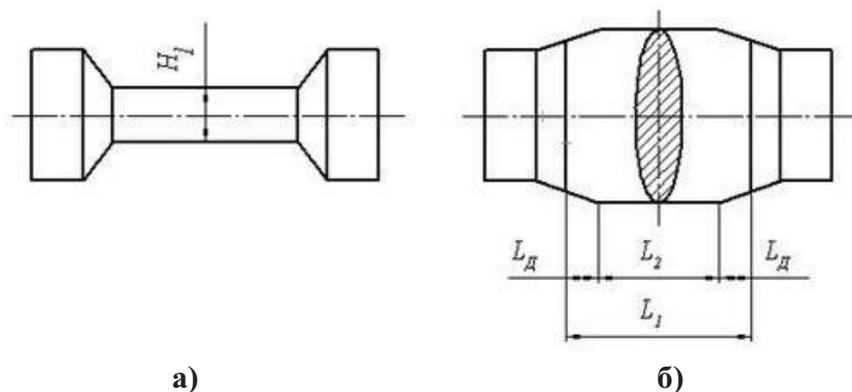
Заготовка с участками незаполнений длиной L_D после вальцовки по схеме круг-овал: а – вид сбоку, б – вид сверху
